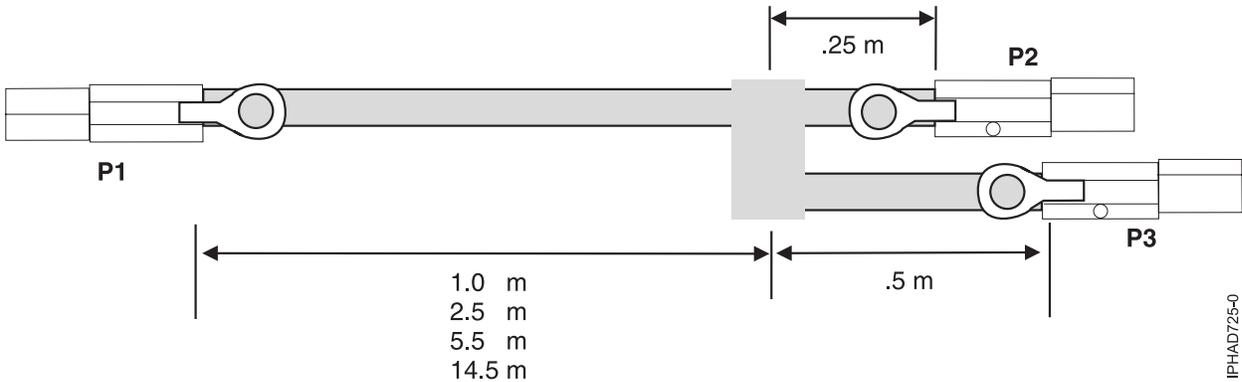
Comprimentos de Cabos de Montagem do Cabo SAS YO Externo
